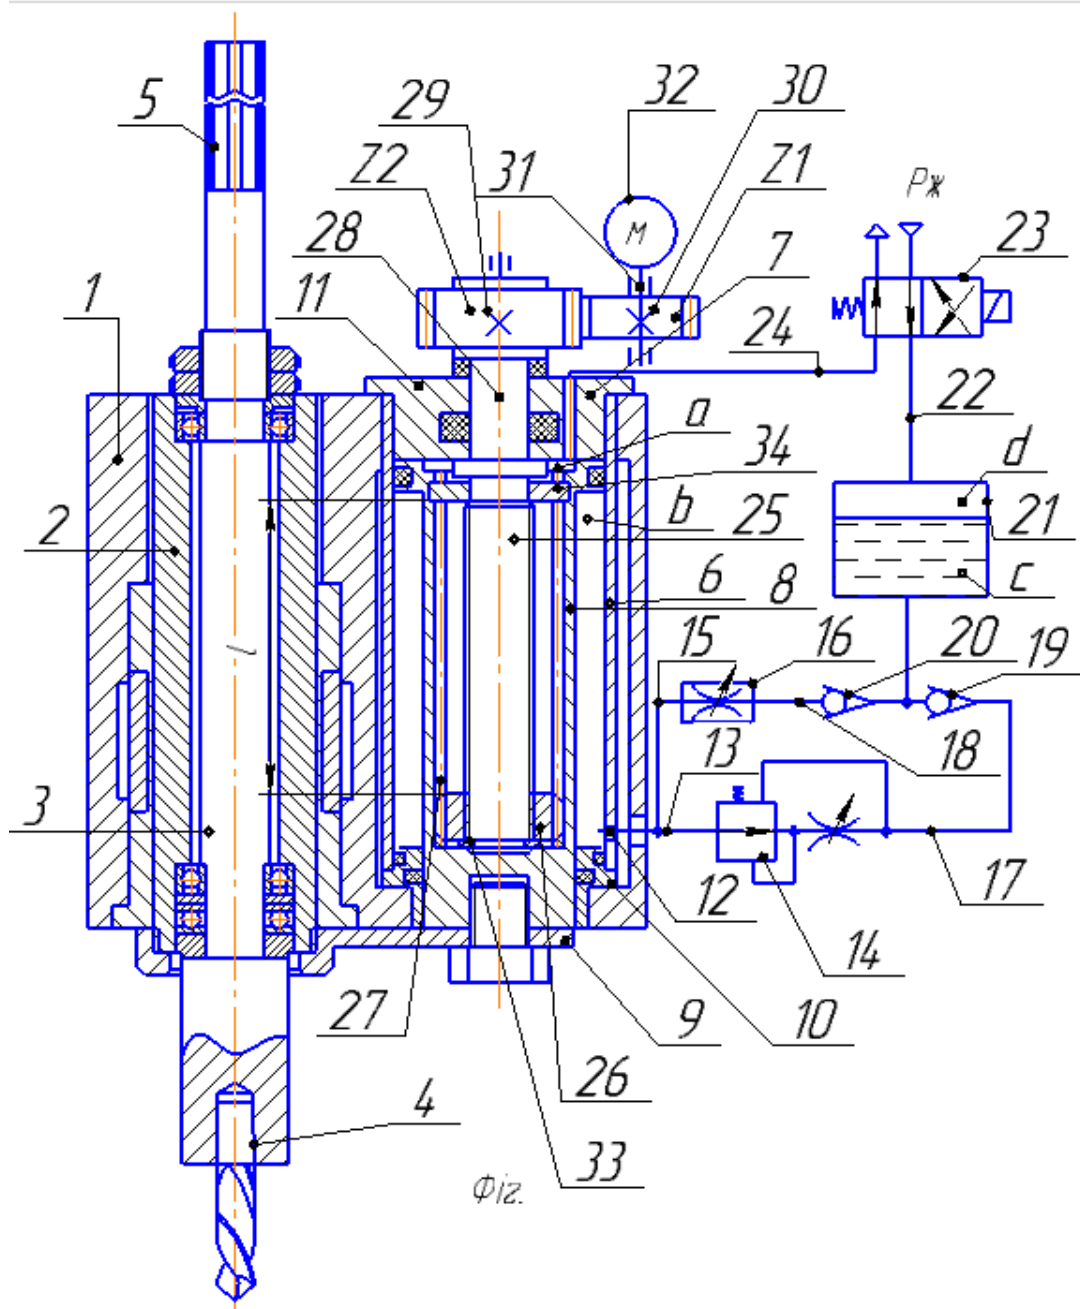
Привод подачі шпинделя свердлильного верстата.
